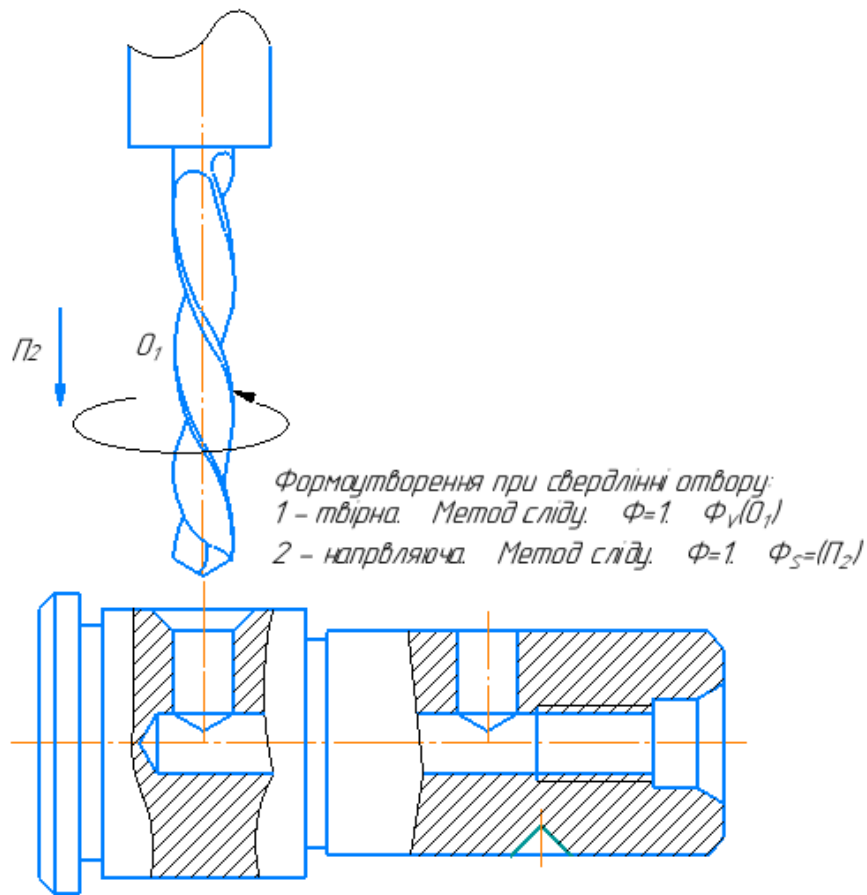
Свердління при нерухомій заготовці та рухомому свердли з його поздовжньою подачею (набір ФУР)
